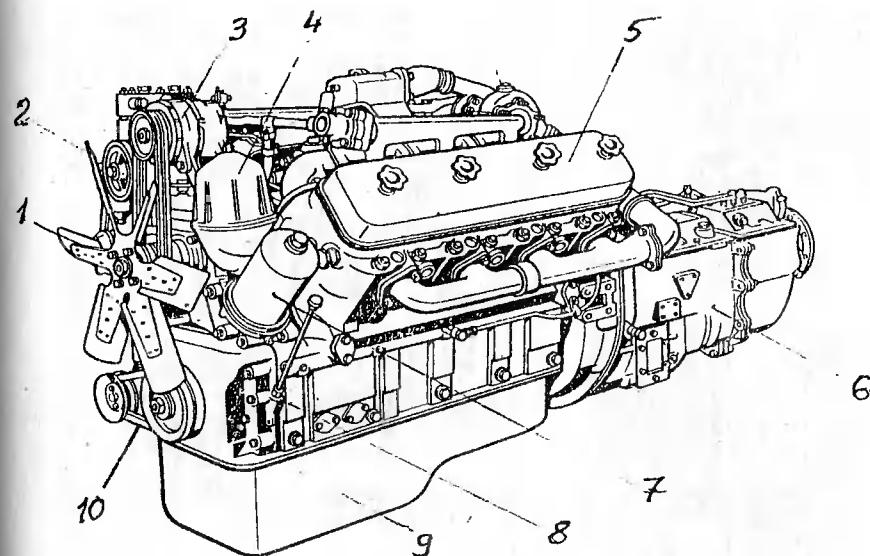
Двигатель ЯМЗ-236; ЯМЗ-238:
